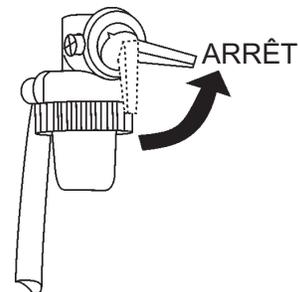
Culbuteur de carburant du moteur (ARRÊT)
